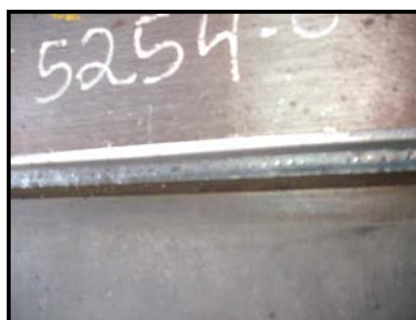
Corpo de prova após a execução do primeiro passe de soldagem ou passe de raiz.
